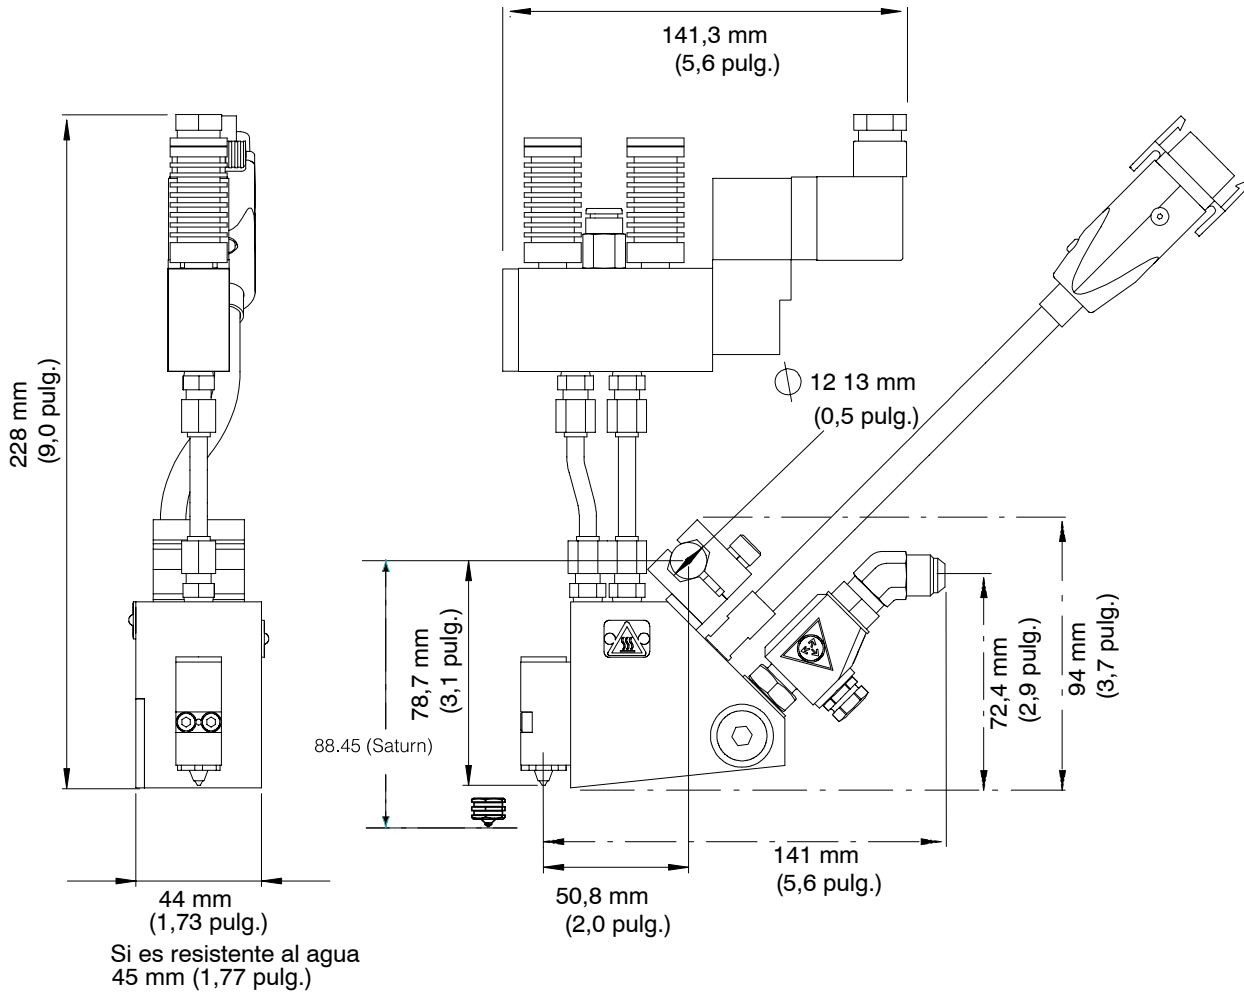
Dimensiones de una pistola configurable de un módulo con una electroválvula SG
